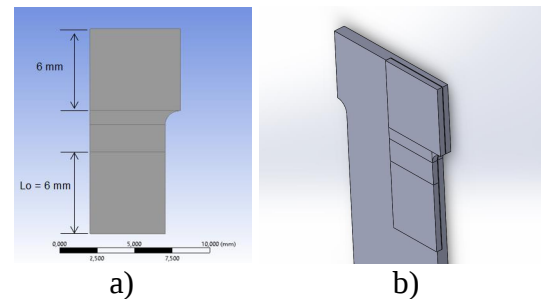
Probeta simulada a) 1/8 de toda la probeta, b) ensamble. Fuente: elaboración. propia.
